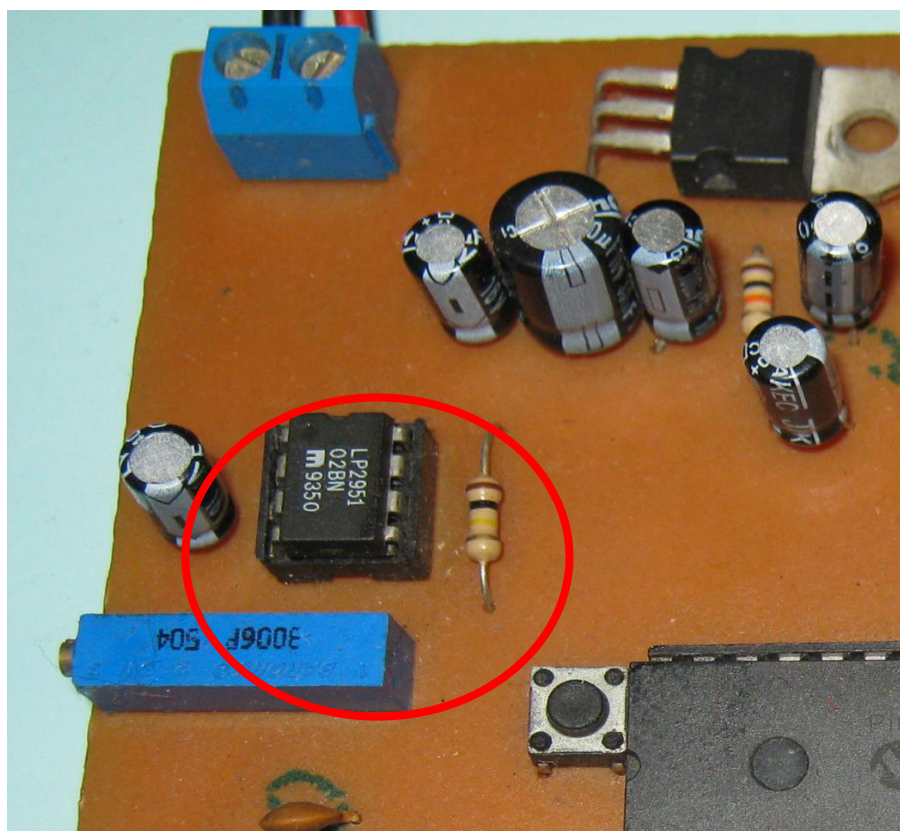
Regulador de Voltaje LP2951 montado en nuestro PCB
